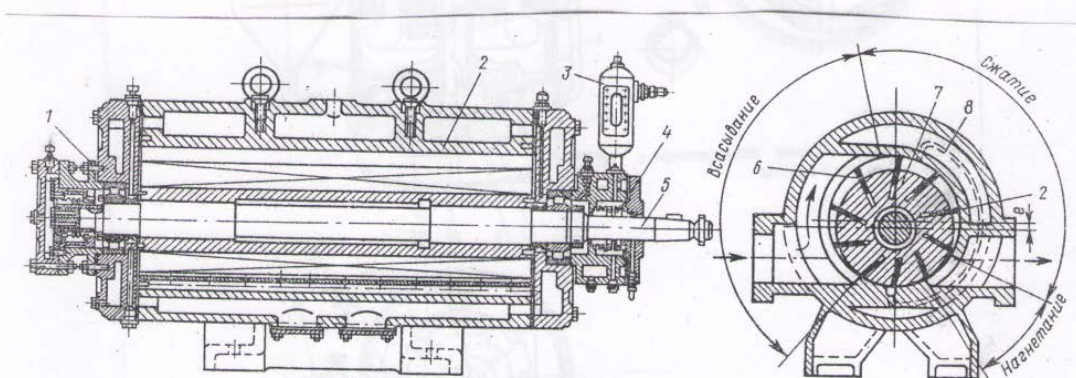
Ротационный пластинчатый компрессор РАБ-300С
